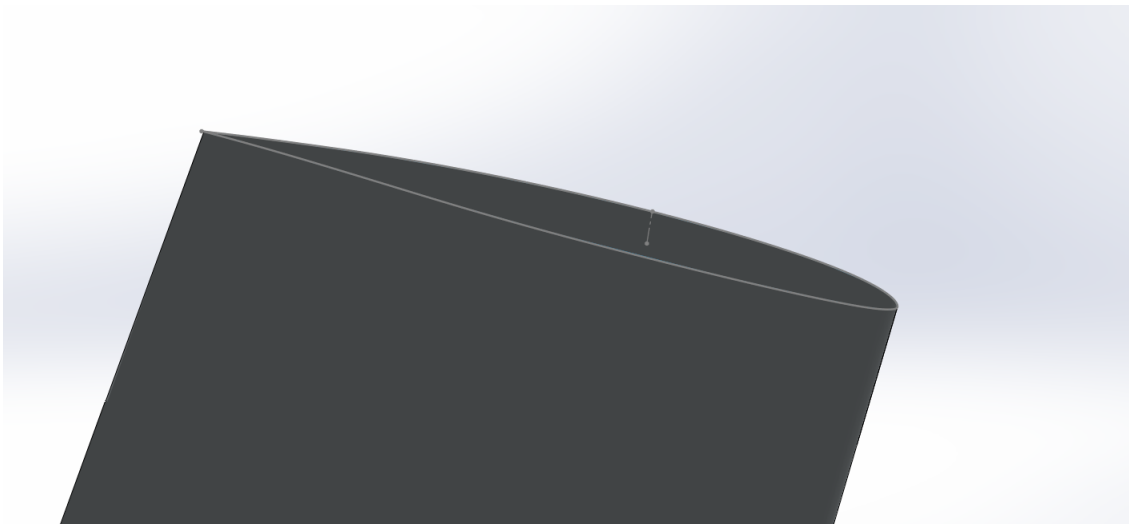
Sélection de plan passant par le dernier profile
